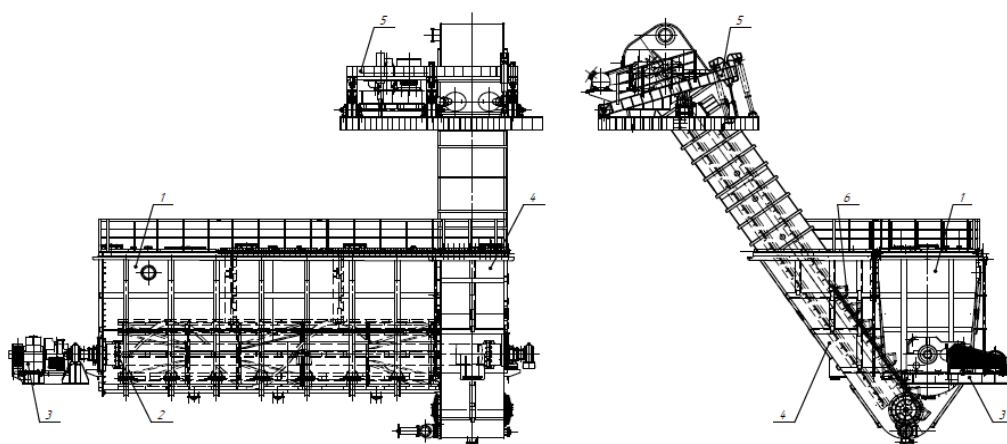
Шнековый растворитель с элеватором: 1 – корпус шнековой мешалки с крышкой, 2 – ротор, 3 – привод шнековой мешалки, 4 – элеватор обезвоживающий, 5 – станция приводная левого исполнения, 6 – цепь ковшовая элеватора
